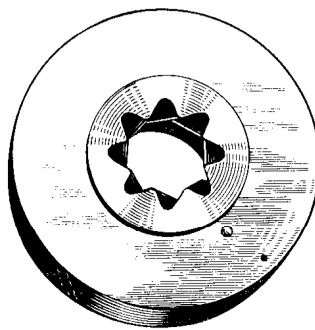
Приспособление для снятия конического упорного подшипника главной передачи
